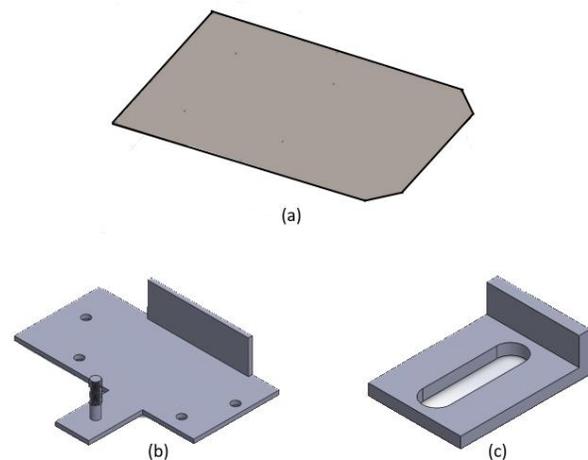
(a) Piso del buggy; (b) Portador de batería; (c) Sujetador de batería;
